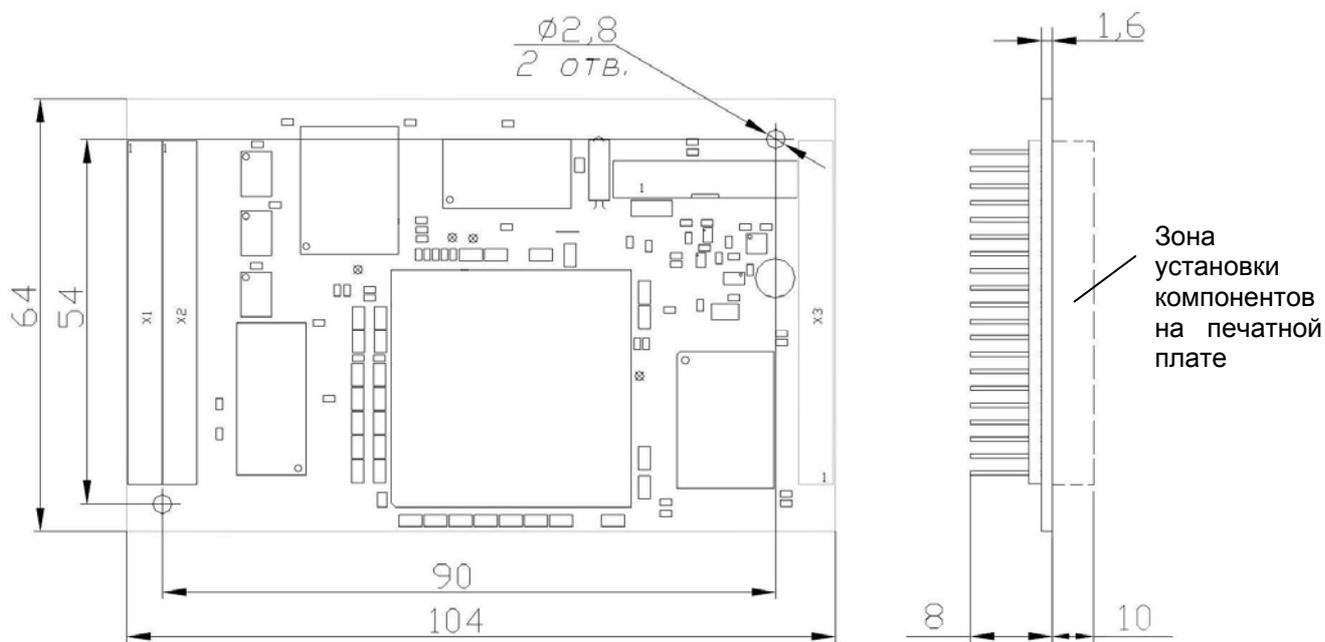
Габаритно-присоединительные размеры модуля t-mezon с односторонними штырями (для справки)
